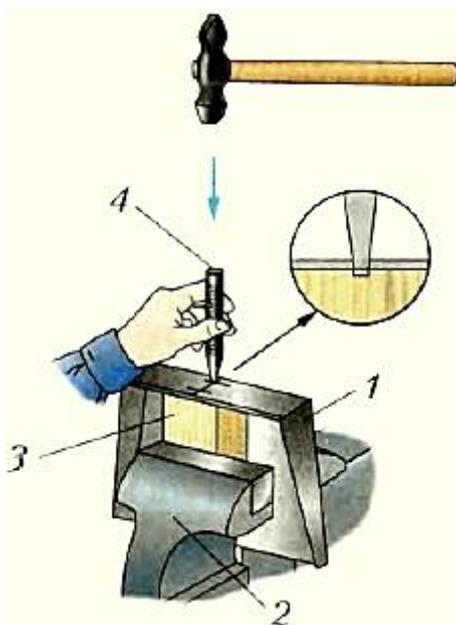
Пробивание отверстий бородком: 1 — заготовка; 2 — тиски; 3 — деревянный брусок; 4 — бородок (пробойник)
